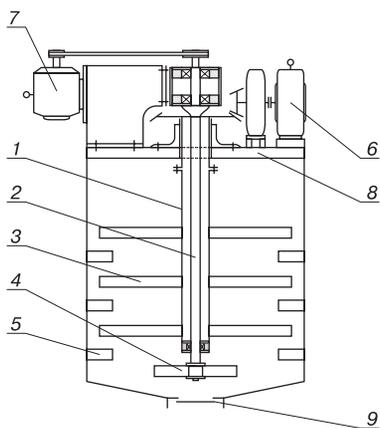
Схема смесителя: 1 – полый вал; 2 – скоростной вал; 3 – большие лопасти; 4 – малые лопасти; 5 – неподвижные лопасти; 6, 7 – электродвигатели; 8 – сварная рама; 9 – разгрузочный люк
